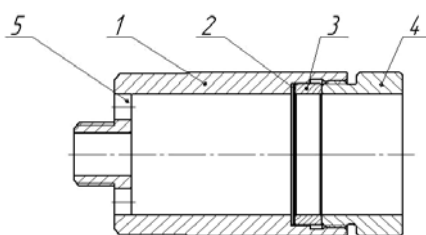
Схема цилиндрического корпуса с аэрационными отверстиями:
